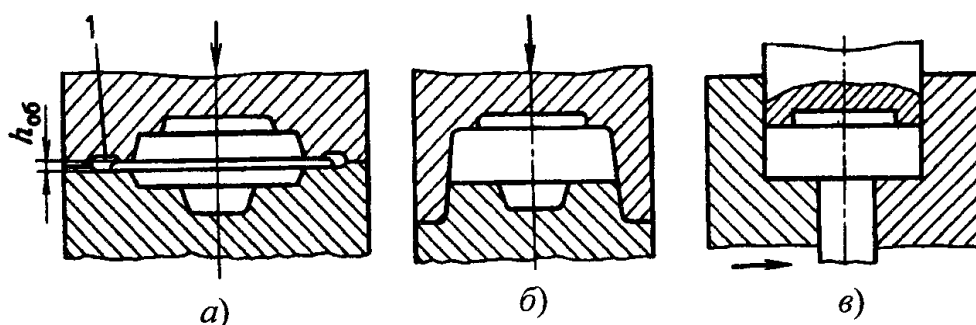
Схемы штамповки в открытых и закрытых штампах: 1 – облойная штамповка
